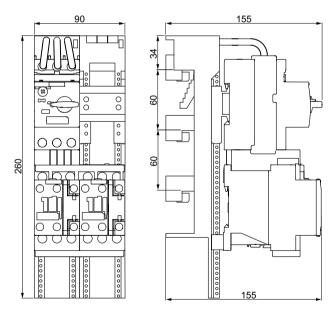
Arrancador inversor S0/S0 y S00/S0, AC, bornes de tornillo 3RA2220-..D..-0AP0
